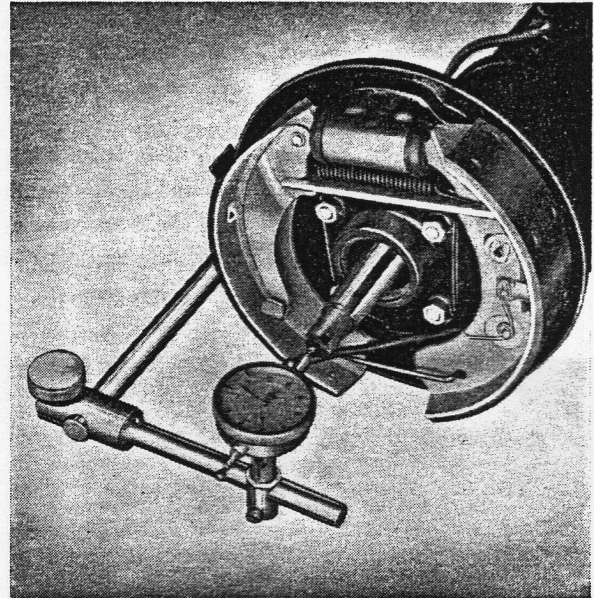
Aufmessen des Axialspieles für die Achswellen
